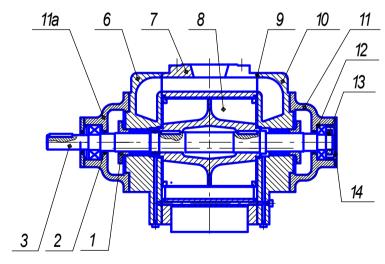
Разрез вакуум-насоса и компрессора типоразмерного ряда
